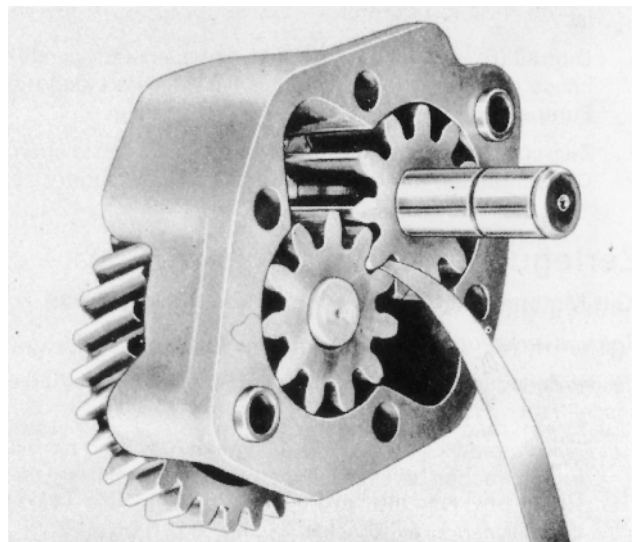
Kontroll av kuggflankspel (0,15-0,35 mm)
